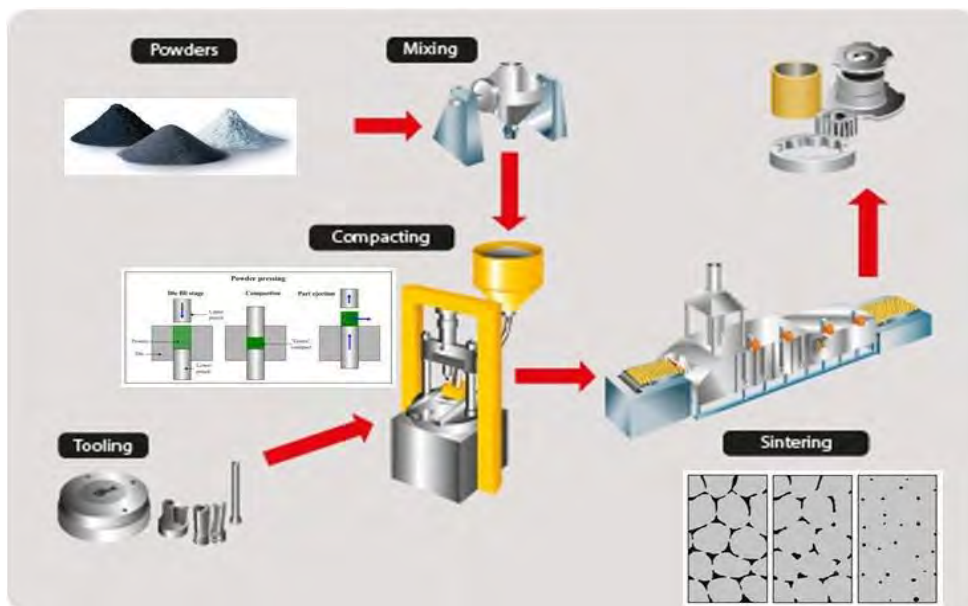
Схема роботи з порошковими матеріалами
